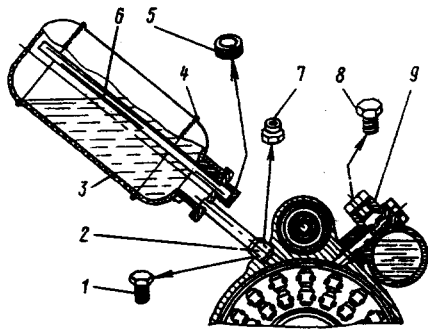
Заливка масла в осевой шарнир втулки рулевого винта приспособлением 8-100 (ЭКС-1):
